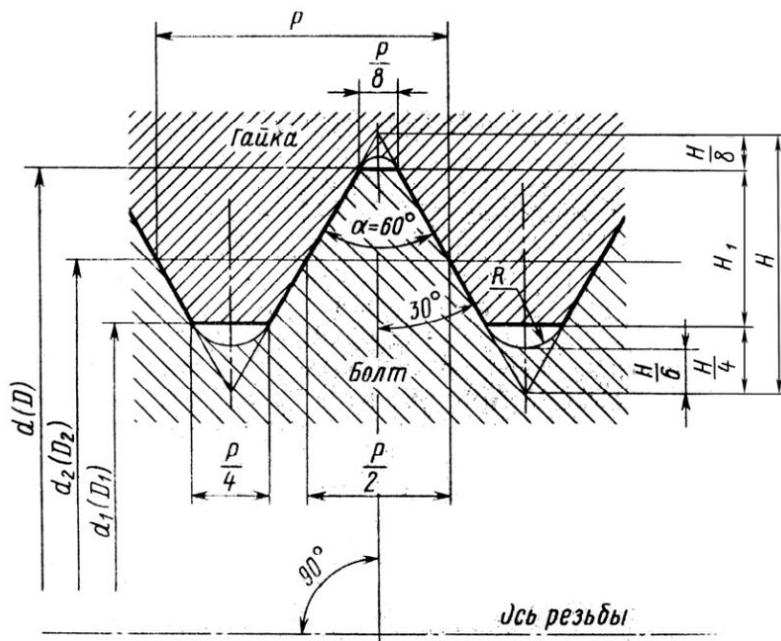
Профиль и параметры метрической крепёжной резьбы
